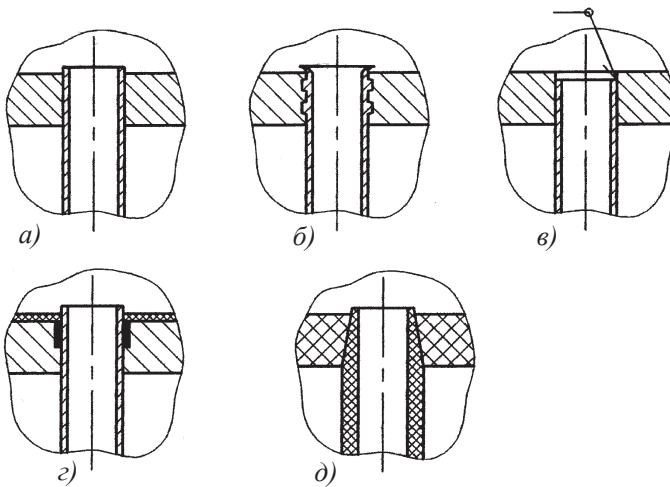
Крепление труб в трубной решетке: *а* — гладкая развальцовка; *б* — развальцовка в канавки с отбортовкой; *в* — приварка труб; *г* — пайка мягким припоем; *д* — склеивание
